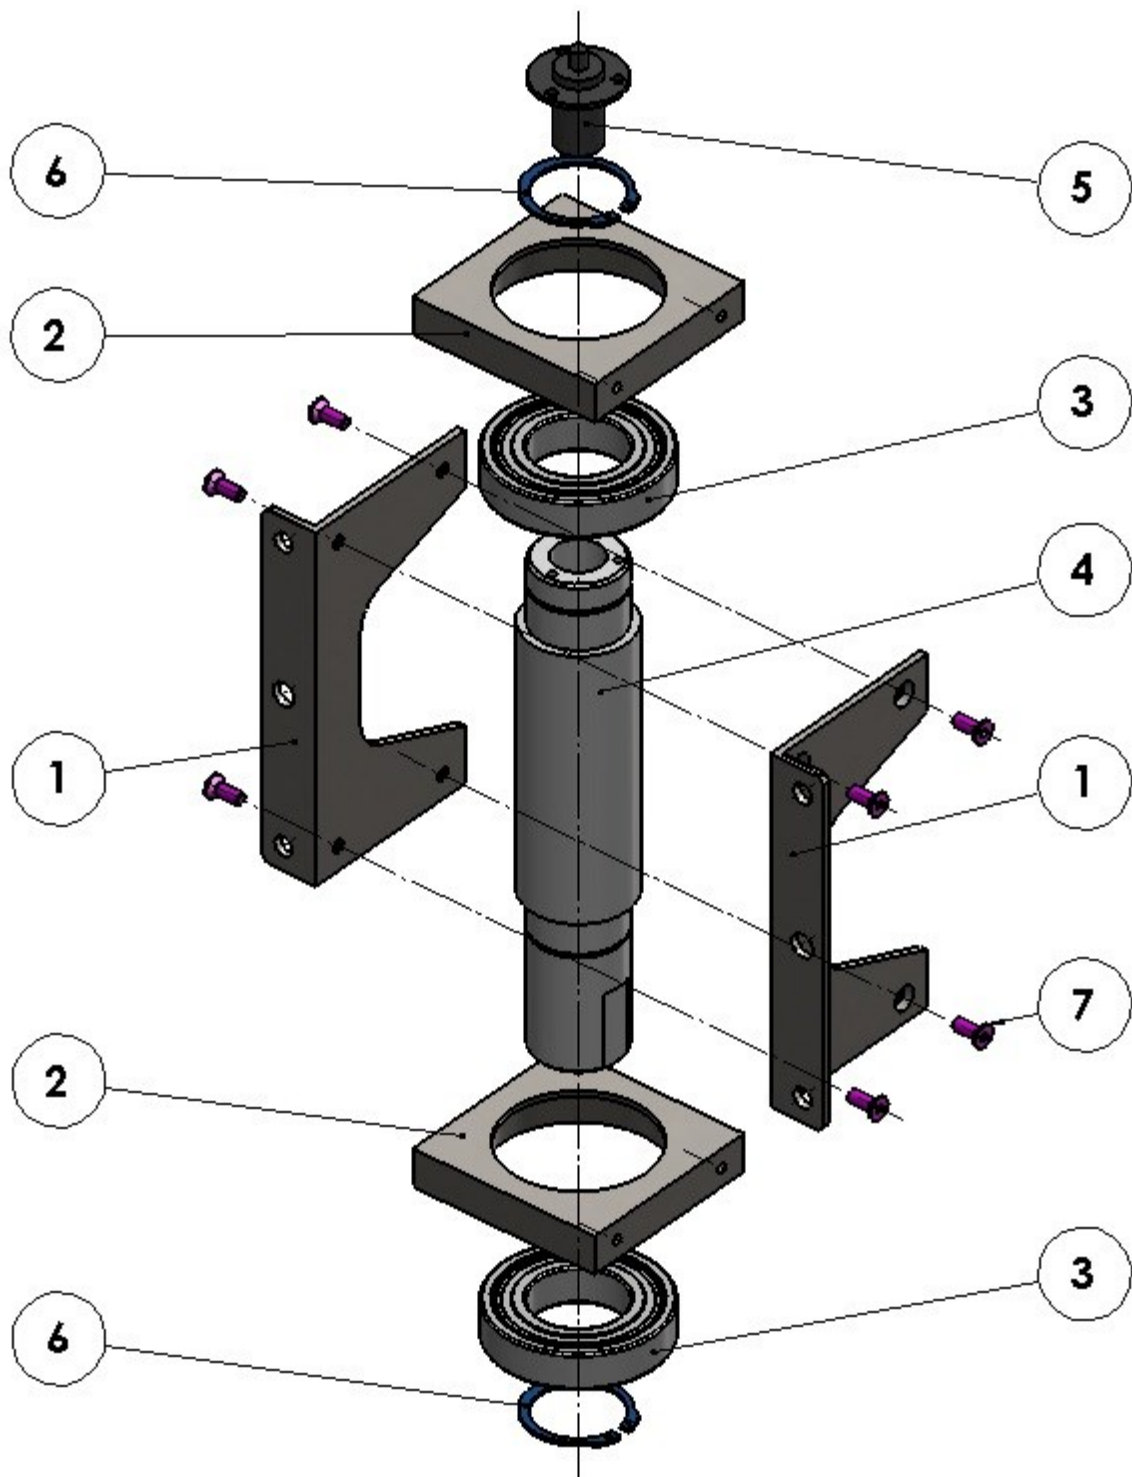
Ansamblul suport turbina - Vedere explodată a ansamblului.
